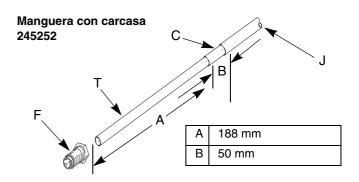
Dimensiones de la manguera para suspensiones acuosas (en la pistola)
